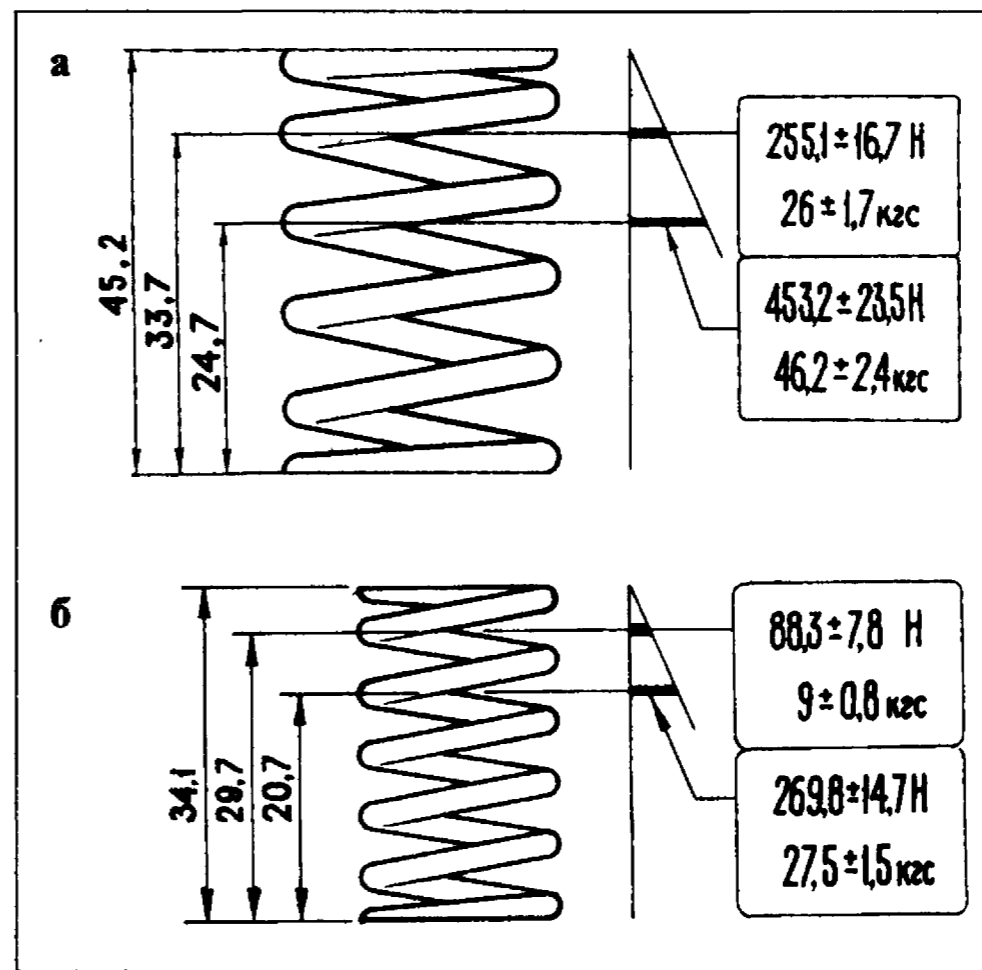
Основные данные для проверки пружин клапанов: а — наружная пружина; б — внутренняя пружина
